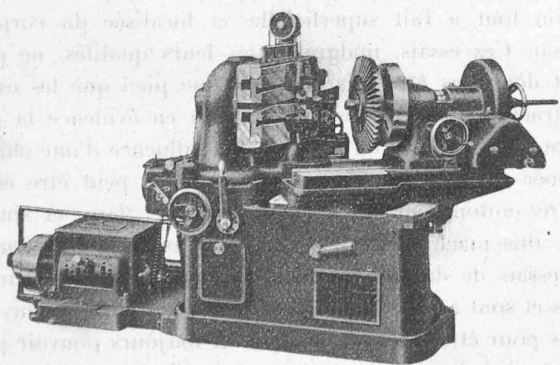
Machine automatique à tailler les engrenages coniques. Modèle n° 2, admettant des engrenages jusqu'à 500 mm. de diamètre primitif.
